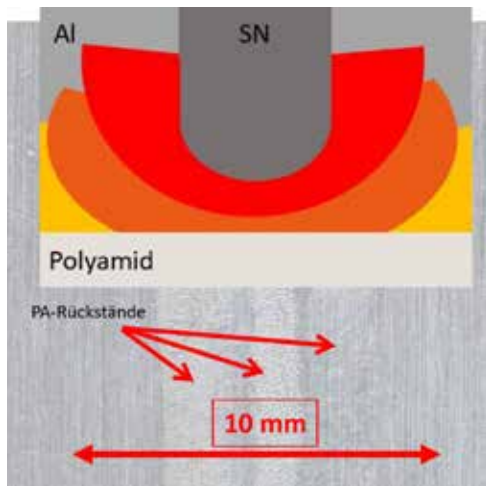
• Wärmeübertragung (schematisch) des aufgeschmolzenen Aluminiums (Al – Aluminium, SN – Schweißnaht) mit gleichzeitiger Ansicht der abgelösten Aluminiumprobe mit darauf verbliebenen Rückständen des Polyamids.
